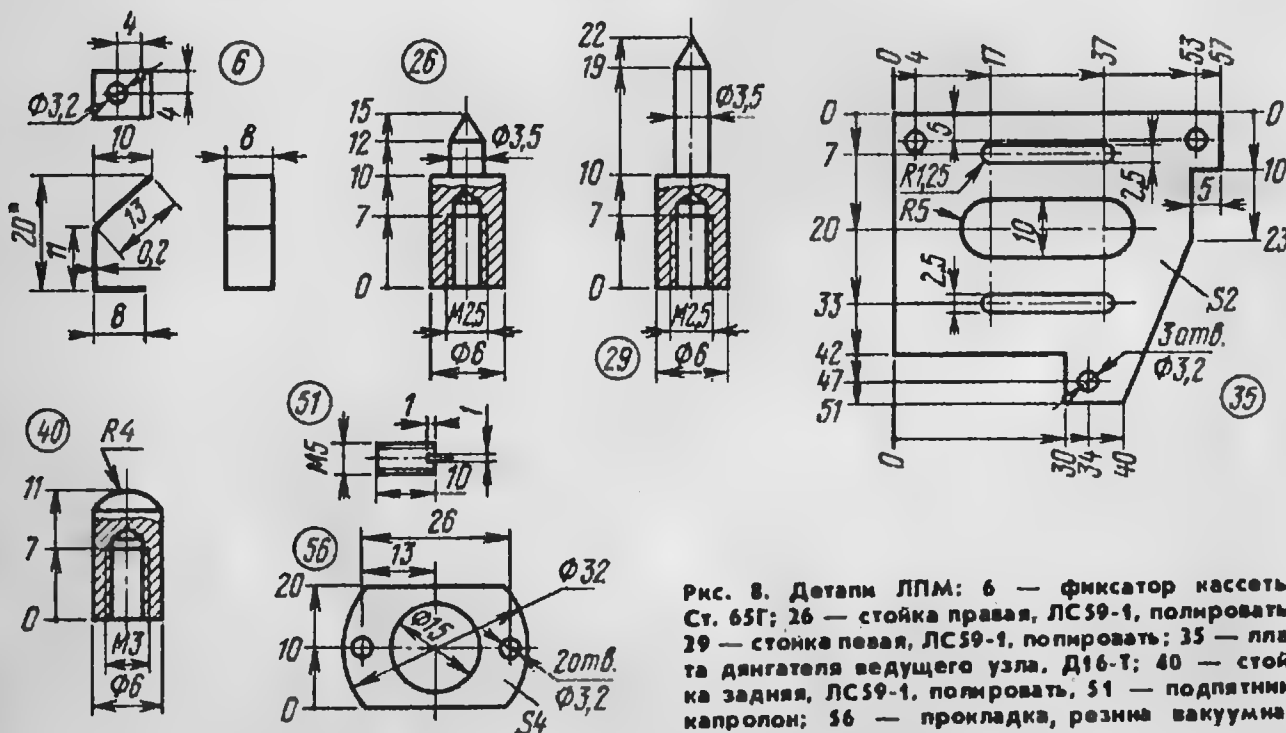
Детали ЛПМ: 6 — фиксатор кассеты, Ст. 65Г; 26 — стойка правая, ЛС59-1, полировать; 29 — стойка левая, ЛС59-1, полировать; 35 — плата двигателя ведущего узла, Д16-Т; 40 — стойка задняя, ЛС59-1, полировать; 51 — подпятник, капролон; 56 — прокладка, резина вакуумная
